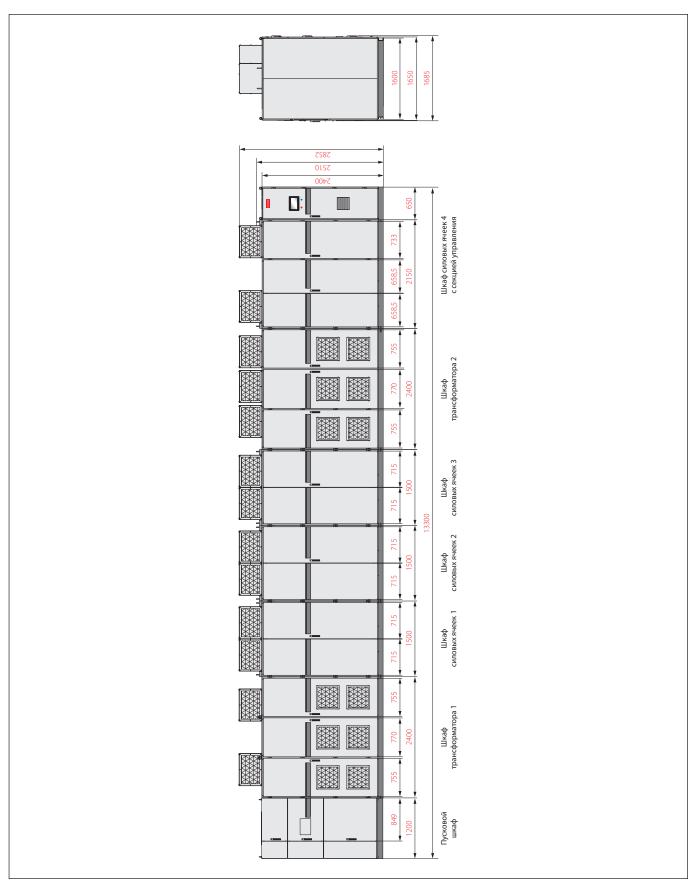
Корпуса DC06 и DD06 на напряжение 10 и 11 кВ
